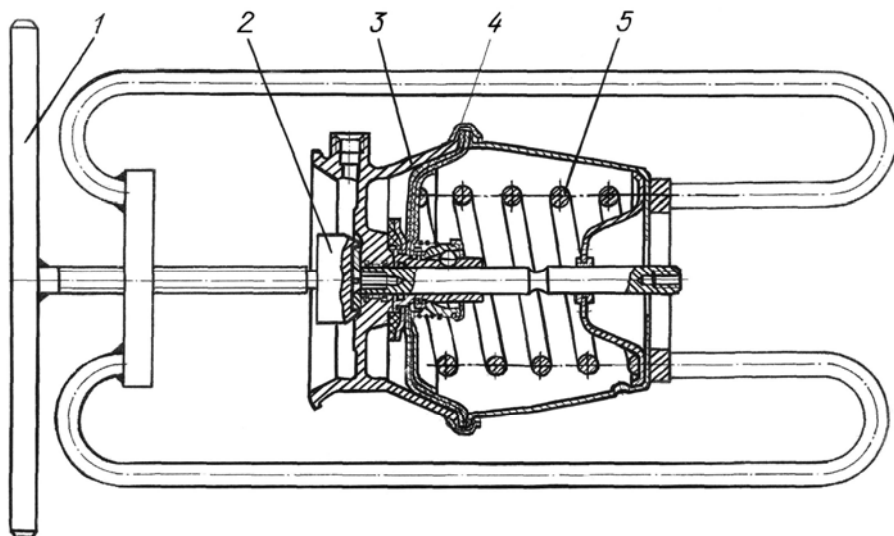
Приспособление для разборки пружинного энергоаккумулятора:
